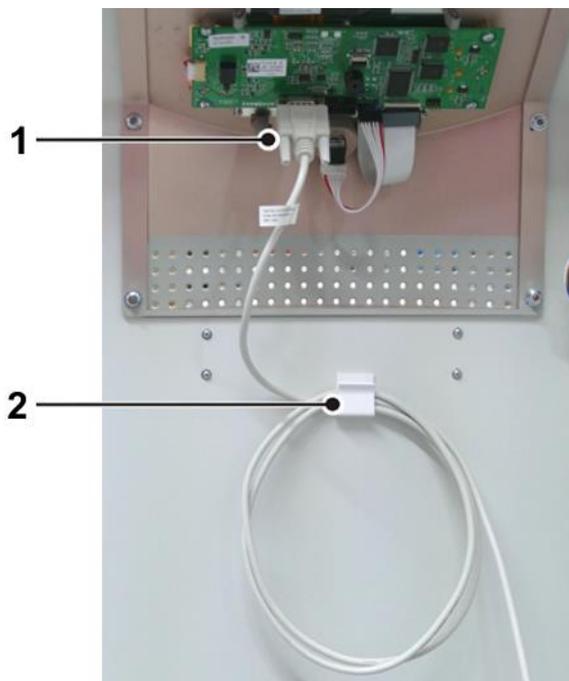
Soporte de cables en el lado interior de la puerta frontal
